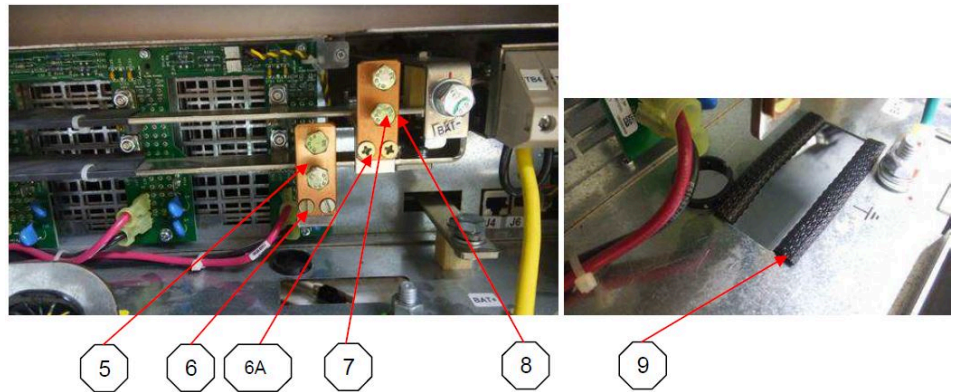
Kit C39165-A7080-B176-1: componentes que se utilizan en la parte trasera
